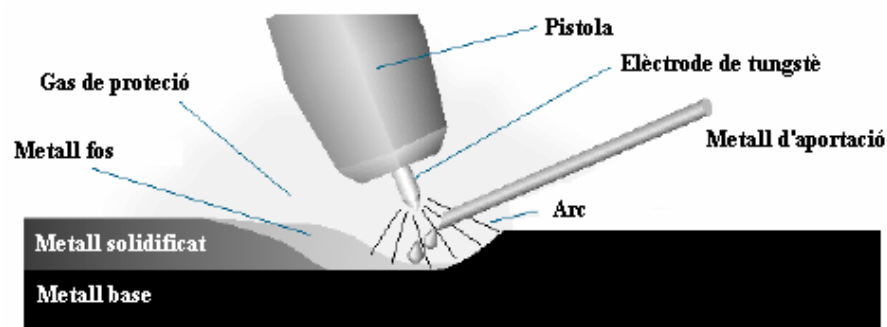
Soldadura de tungstè amb arc elèctric i gas.
